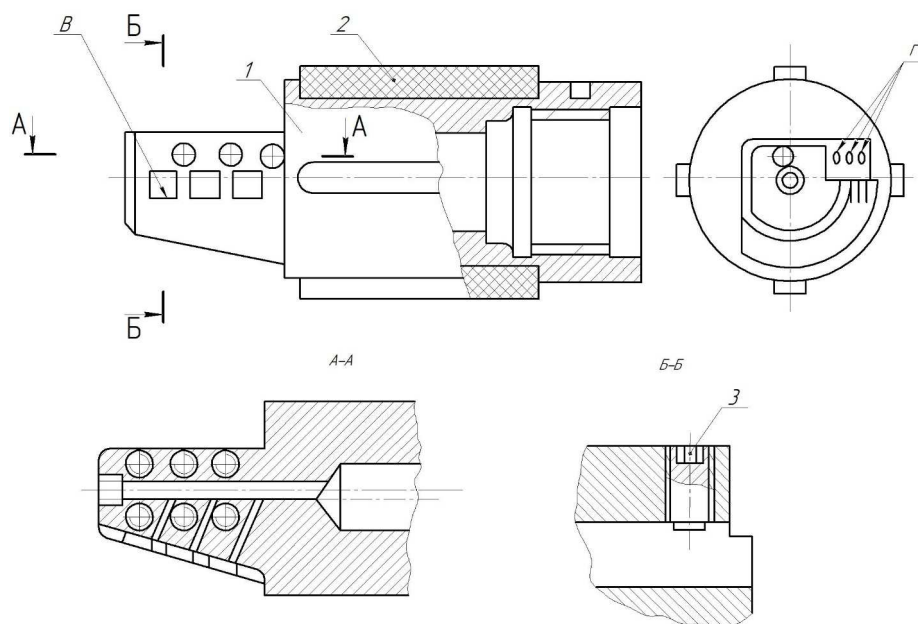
Трехлезвийная головка с деревянными направляющими
